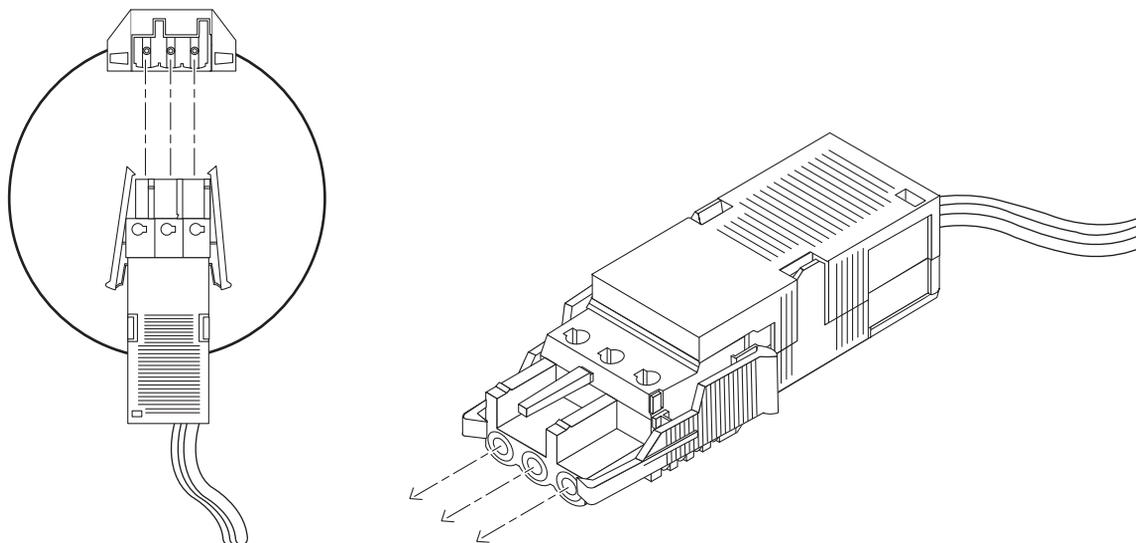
Collegamento del cavo di alimentazione CC in ingresso al connettore CC
